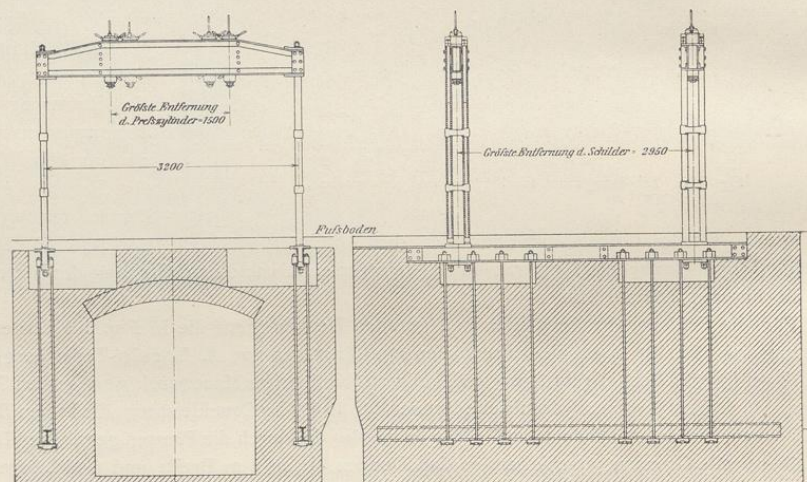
Maschine zur Deckenprüfung von Martens. A. Borsig-Tegel.
